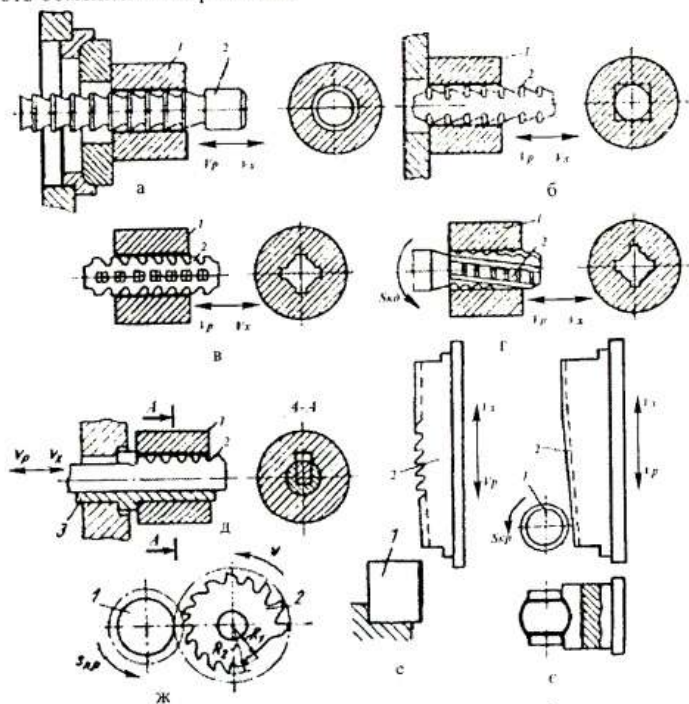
Схеми протягування: 1 – заготовка; 2 – протяжка; 3 – адаптер
